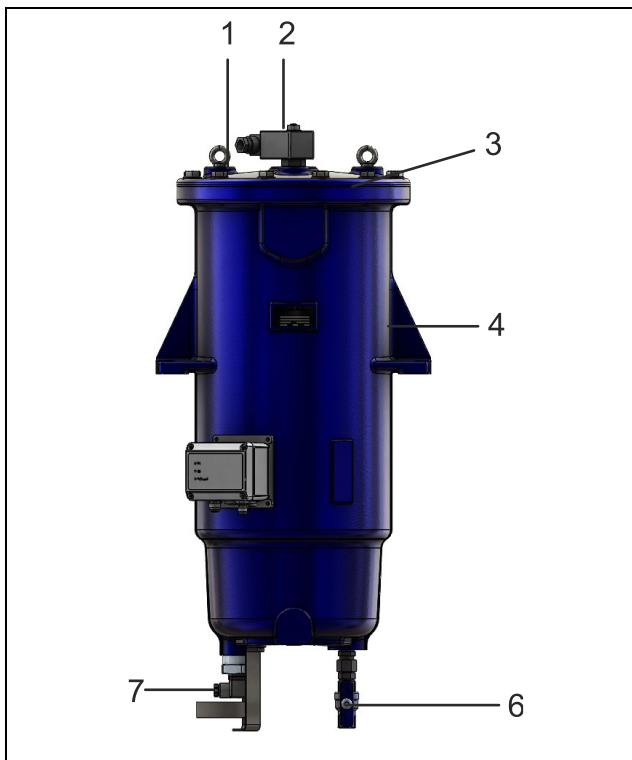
Bezeichnung der Hauptkomponenten (Marine-Ausführung)
